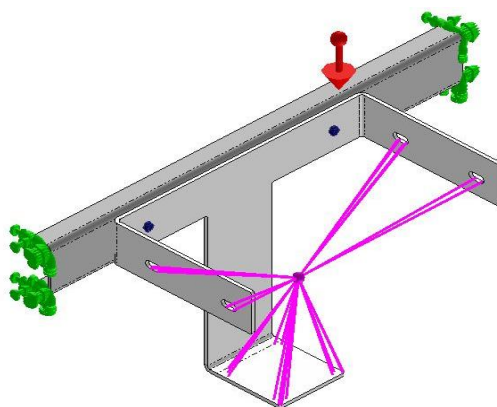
Carga, fixação e aplicação da ligação aparafusada
